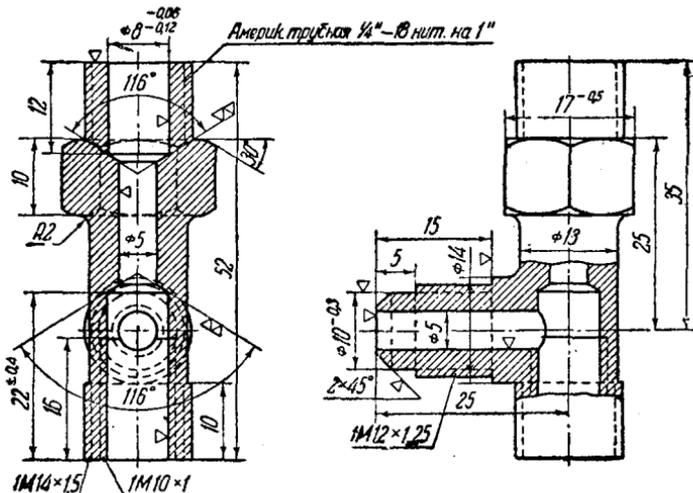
Дет. № 13-17. Корпус вентиля бензинового бака
